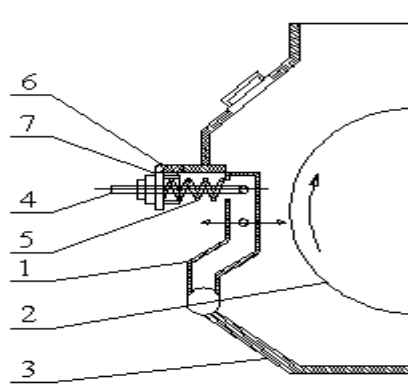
Пластикатор (ПВП): 1 – поверхня пластикатора;
